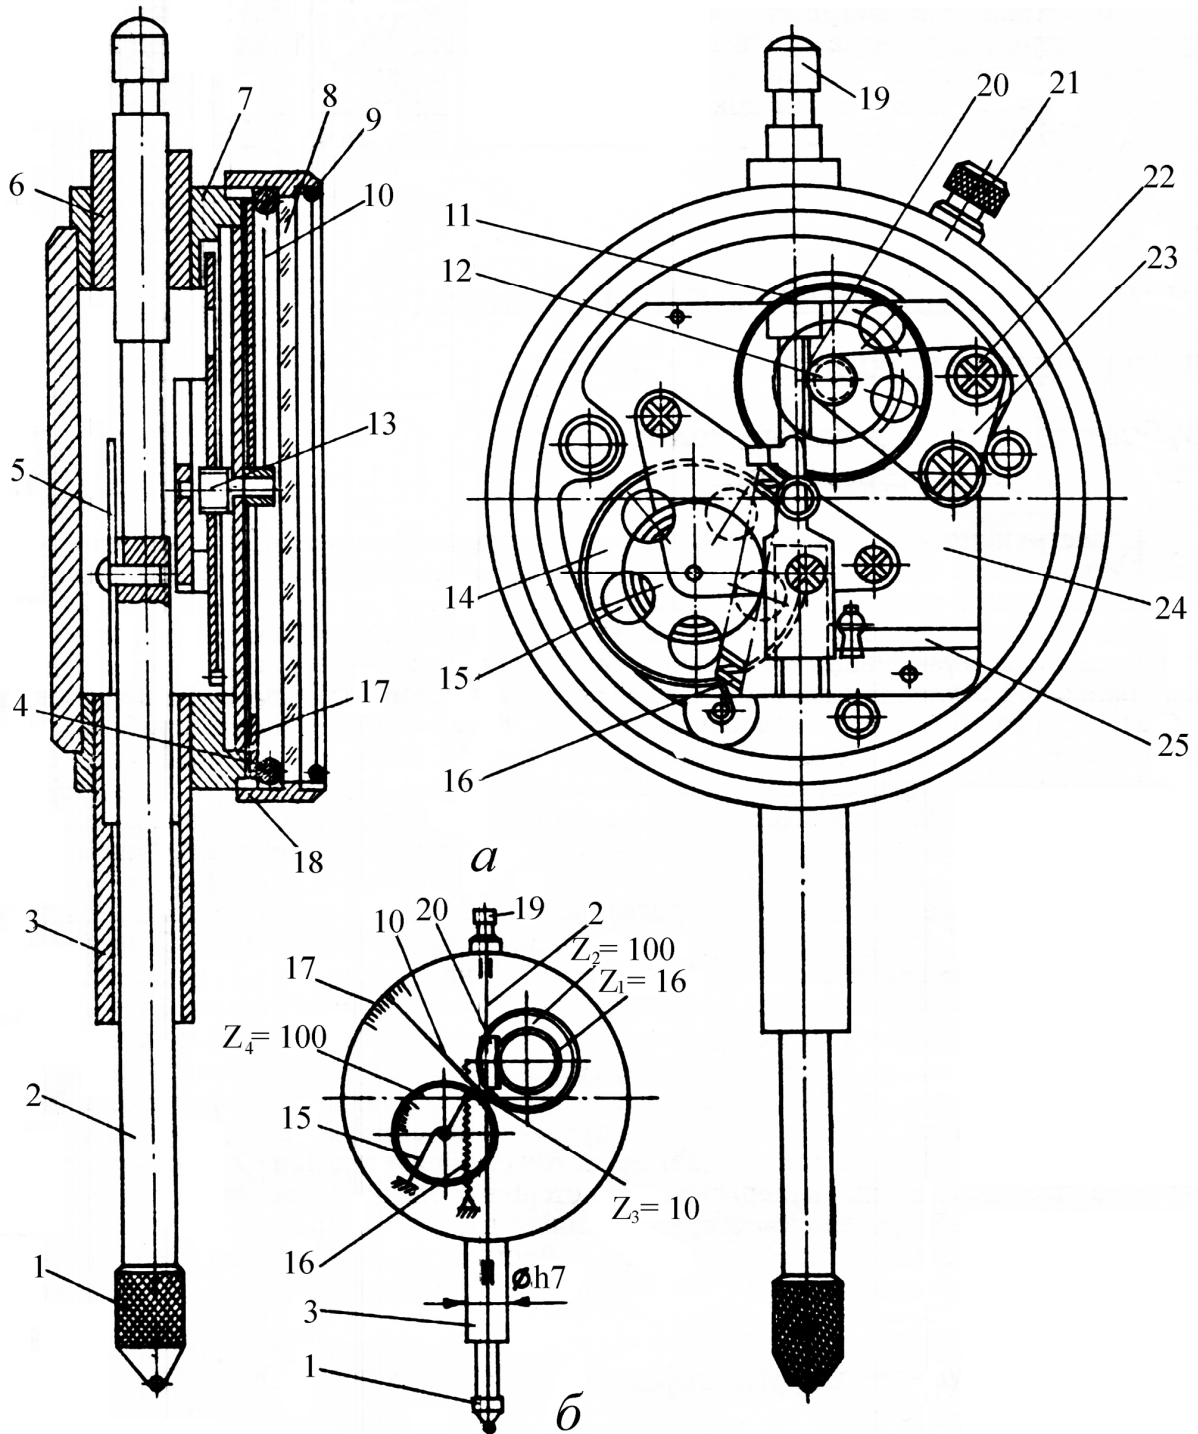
Конструкция (а) и кинематическая схема (б) индикатора часового типа:
